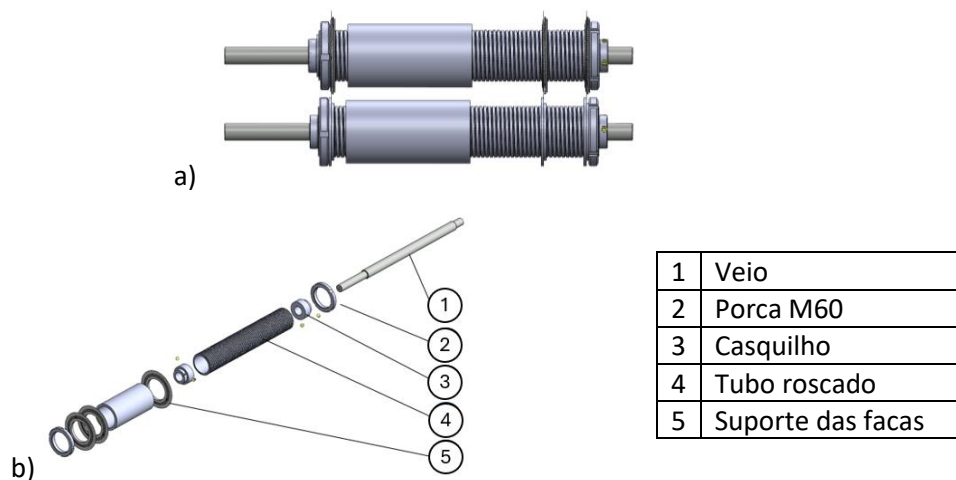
Solução 2: a) vista frontal; b) vista explodida.
